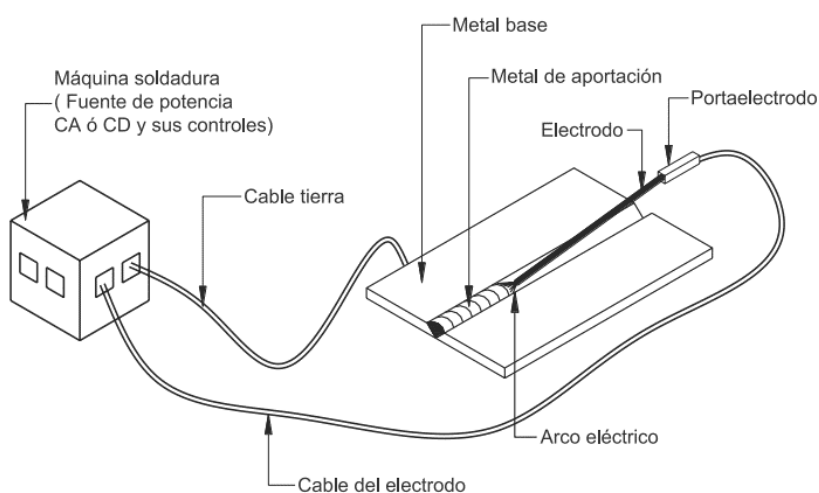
Esquema del equipo para soldadura manual
